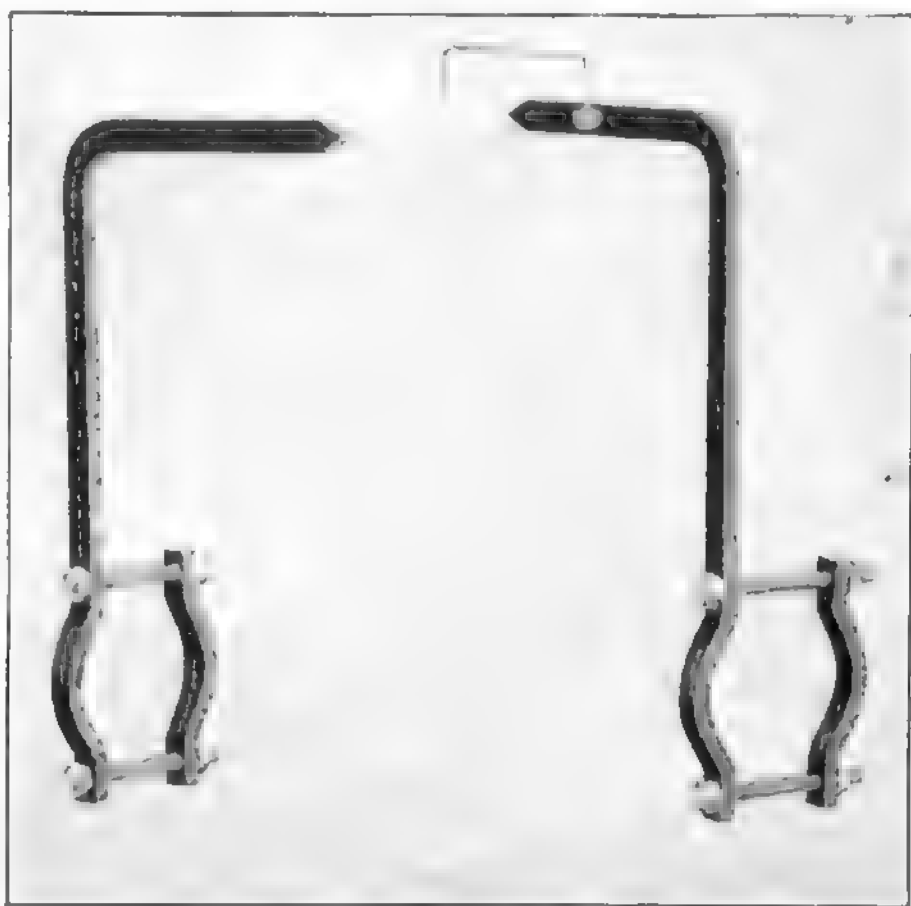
Werkzeug zum Ausrichten direkt gekuppelter Maschinen.
